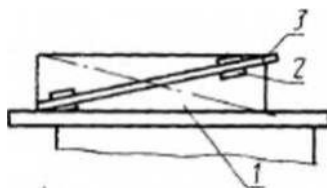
Схема проверки прямолинейности рабочей поверхности направляющей линейки
